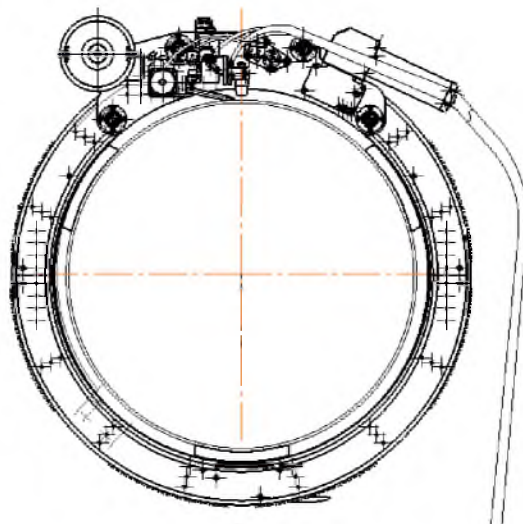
Головка для сварки с подачей присадочной проволоки трубопроводов из алюминиевых сплавов диаметром от 350 до 462 мм
